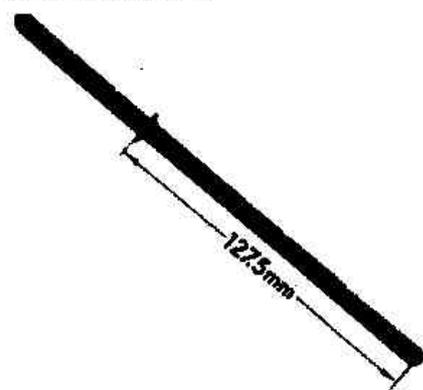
В.16. Шестигранный вал привода масляного насоса (Разд. 29)
